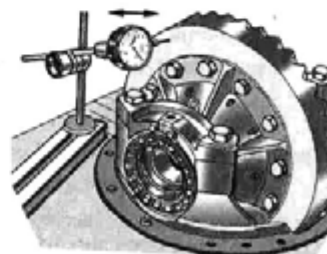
Проверка осевого зазора в подшипниках дифференциала (мост с балкой типа банджо)
